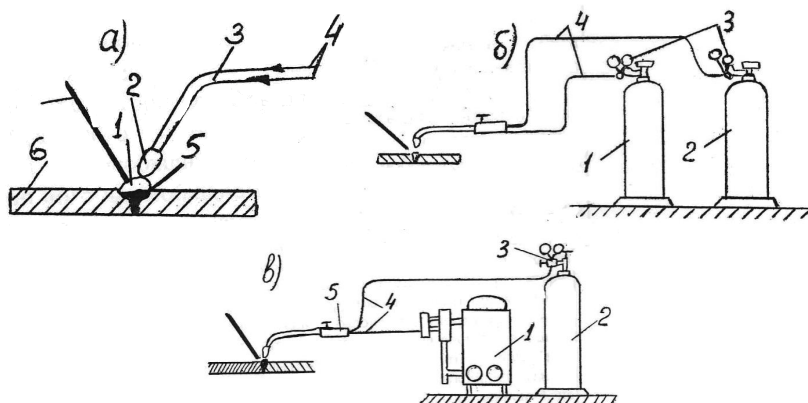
Схема газОВО-кисневого зварювання:
